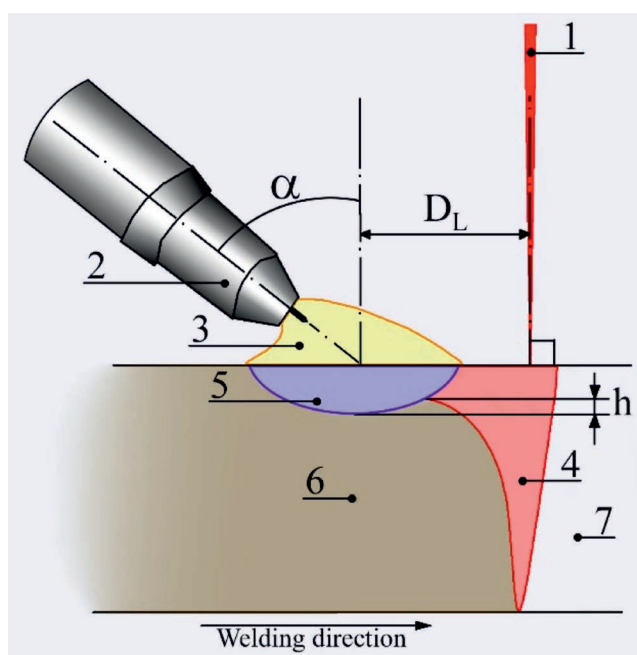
Схема гибридной лазерно-дуговой сварки:
